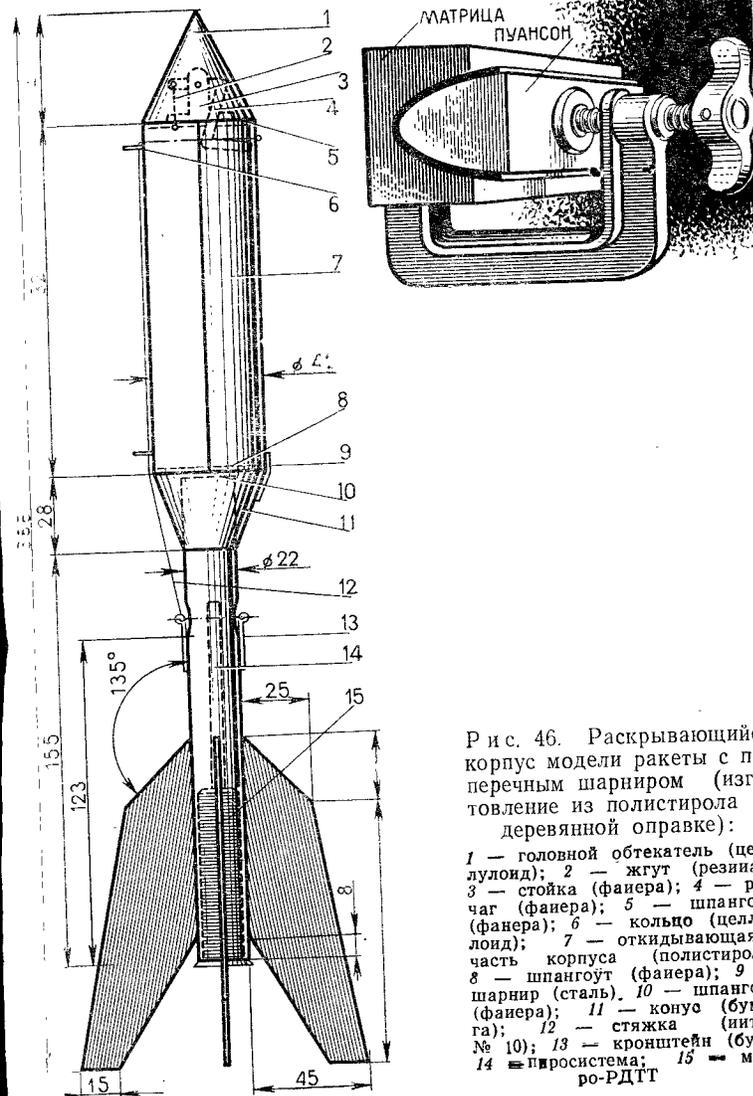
Раскрывающийся корпус модели ракеты с поперечным шарниром (изготовление из полистирола в деревянной оправке):
